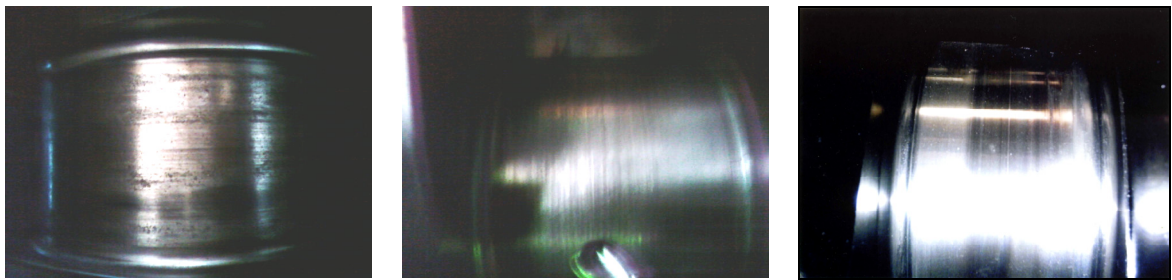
Кольцевой (абразивный) износ шейки коленчатого вала двигателя типа 5Д49
